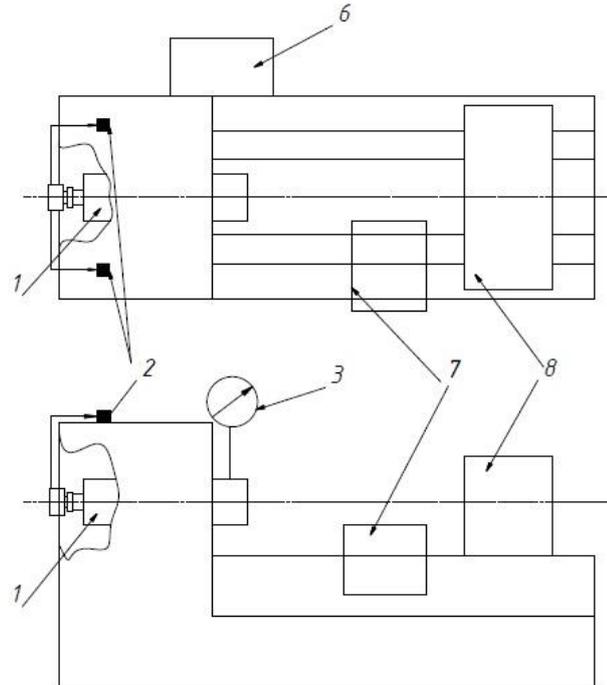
Крепление к станку фазохрометрического датчика ЛИР 158А на консоли с магнитами
